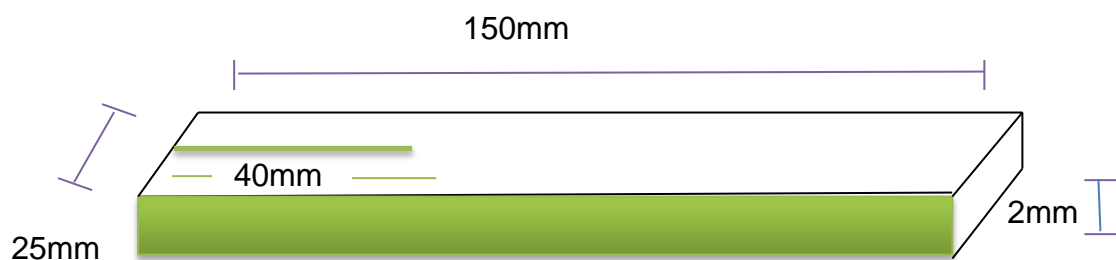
Suaje para prueba de desgarre de 150mm X 25mm X2mm con un corte perpendicular de 40mm al centro.
